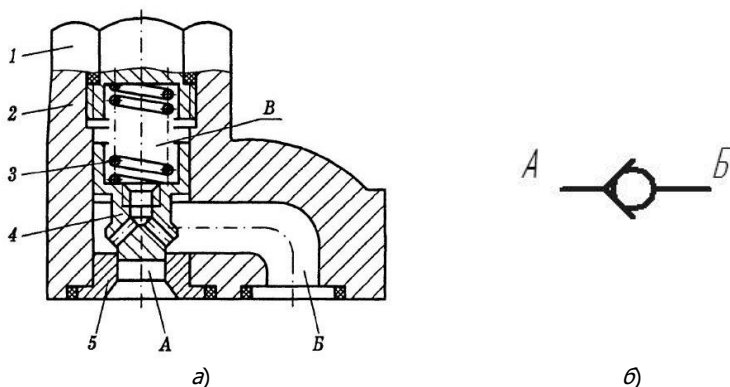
Обратный клапан: а – конструктивная схема; б – условное обозначение
